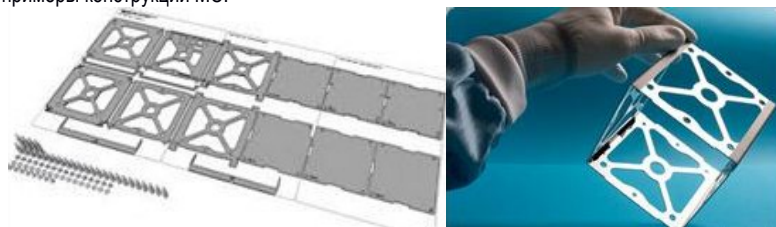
Пример реальных конструктивных деталей корпуса МС
